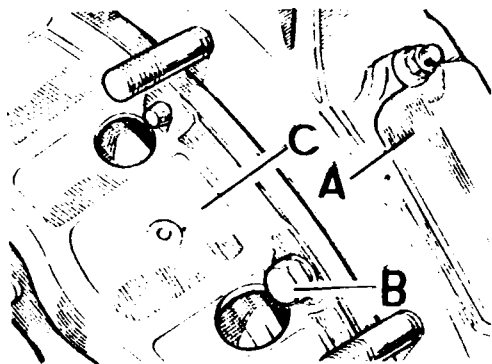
Desmontaje del plato de -- presión y disco de embrague
